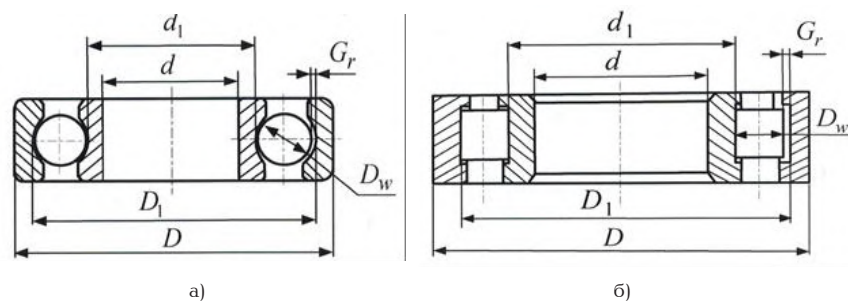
Параметры подшипников при измерении радиального зазора G_r : а) шарикоподшипник; б) роликоподшипник
